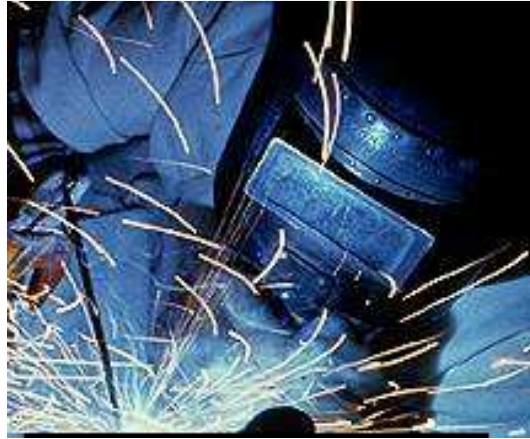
APLICACIÓN DE SOLDADURA ELÉCTRICA
